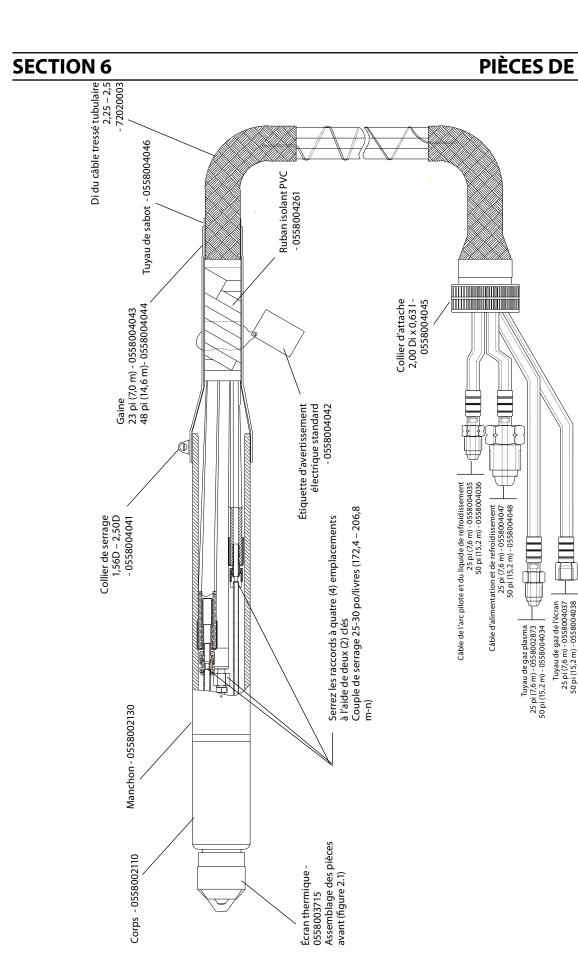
Pièces de rechange - ensemble de la torche PT-26 en ligne
